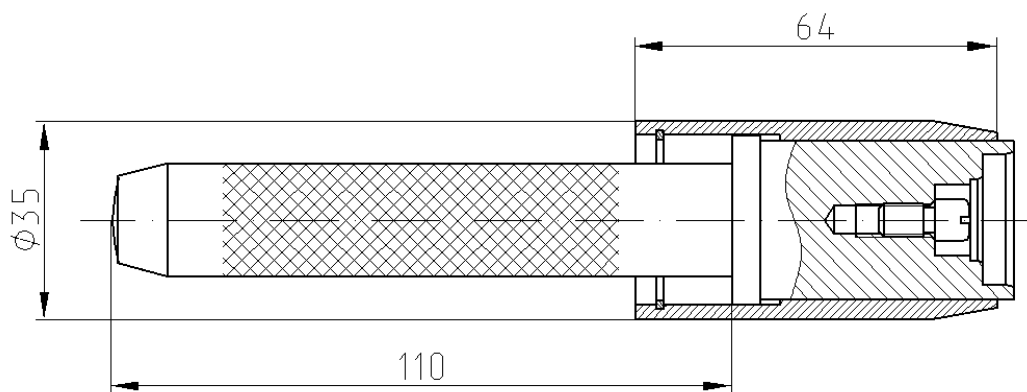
ЗМ 7853-4355, Оправка для напрессовки
